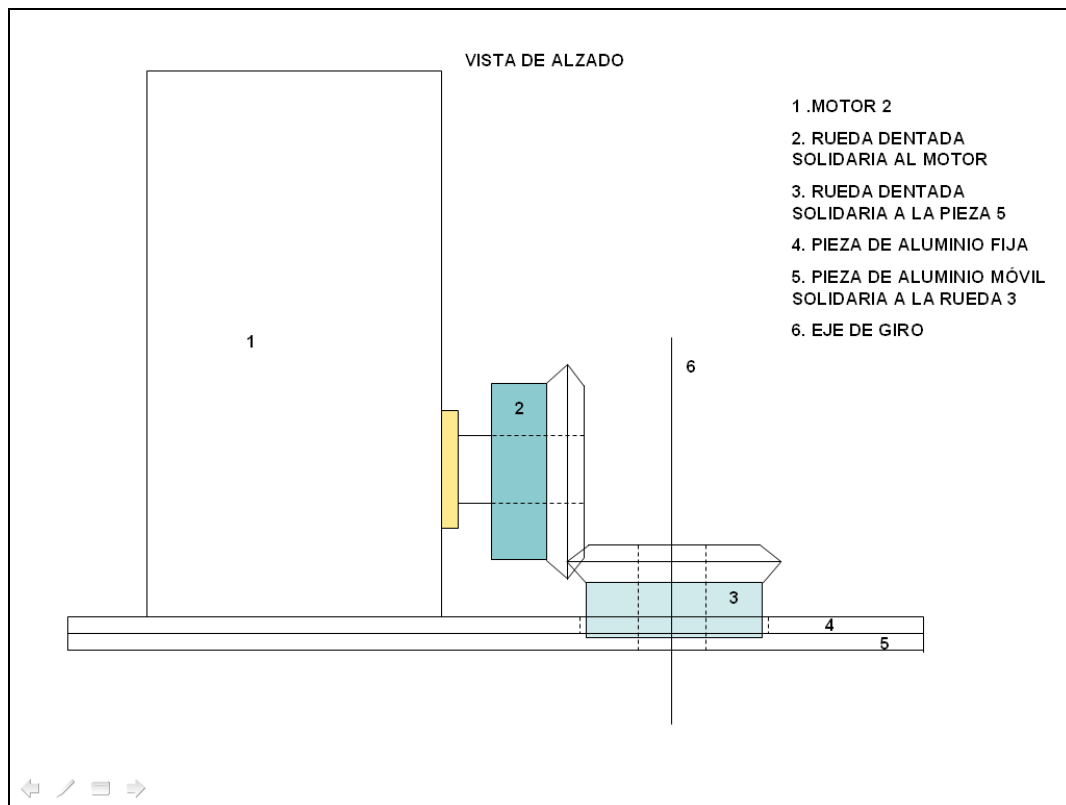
Esquemático de posicionamiento de engranajes del motor 2
